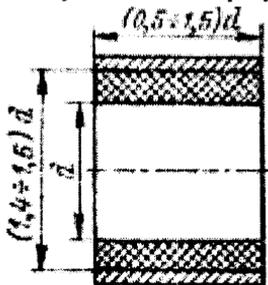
Металлокерамический подшипник, пропитанный маслом с металлокерамической втулкой, запрессованный в стальную обойму
